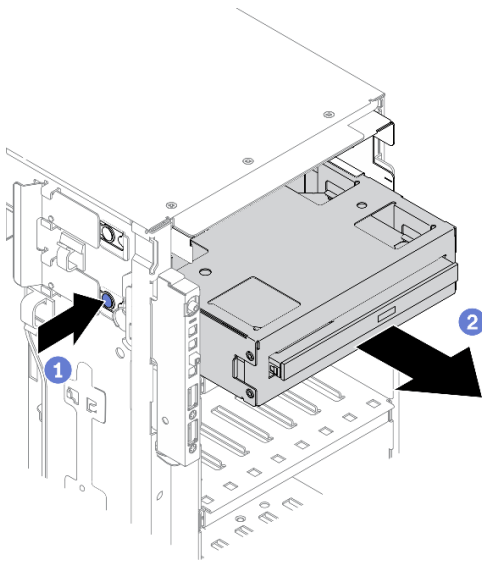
Entfernen der Adapterbaugruppe für eine 5,25-Zoll-Laufwerkposition
